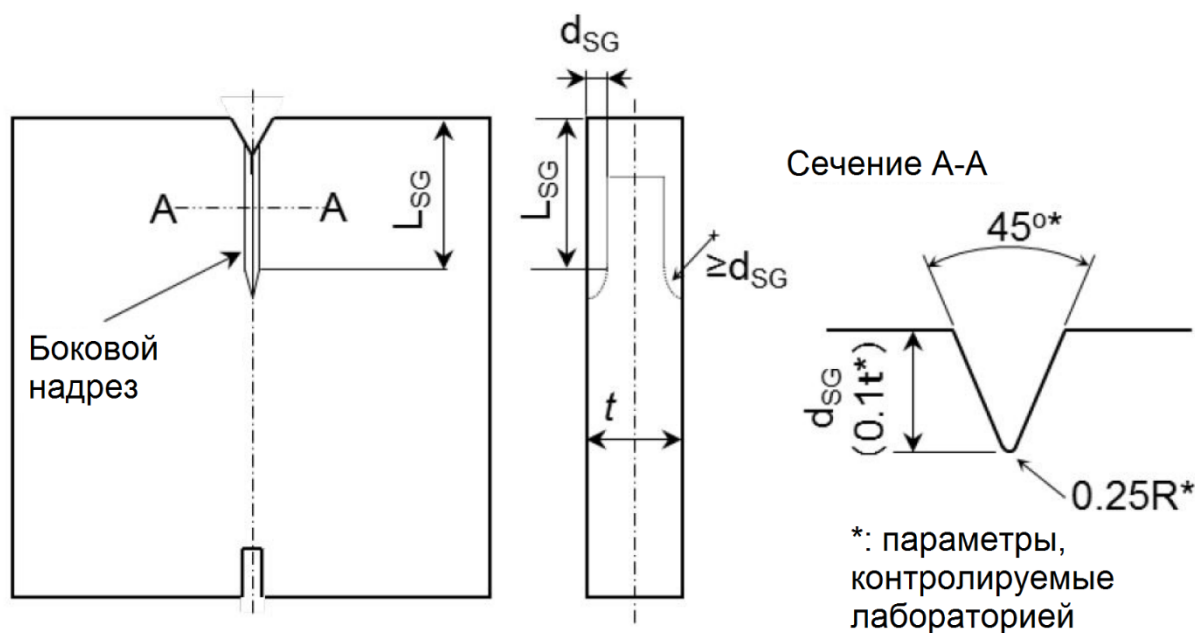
Форма и размеры бокового надреза
